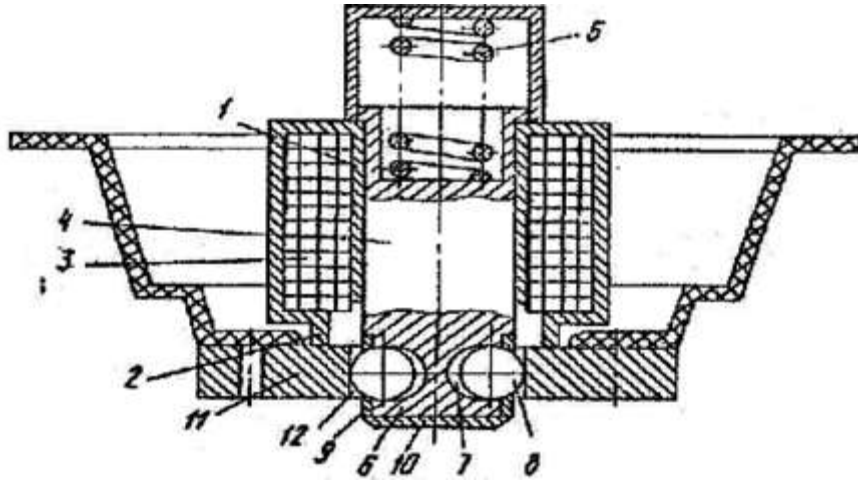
Електромагнітний захват в положенні захвату деталі
